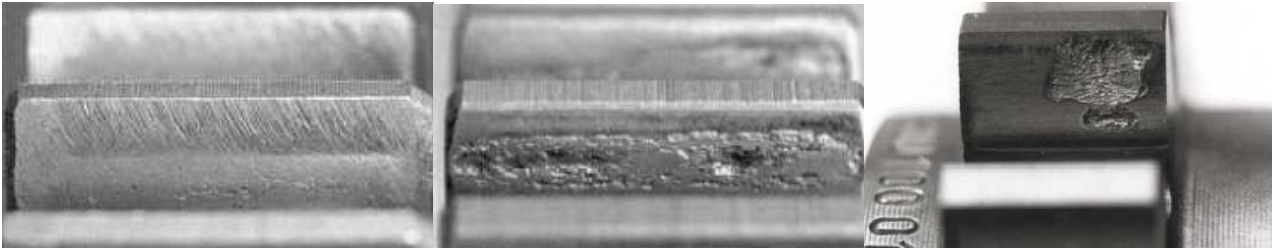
, 4.2.5, 4.2.6 – Pitting iniziale, pitting progressivo, flake pitting
